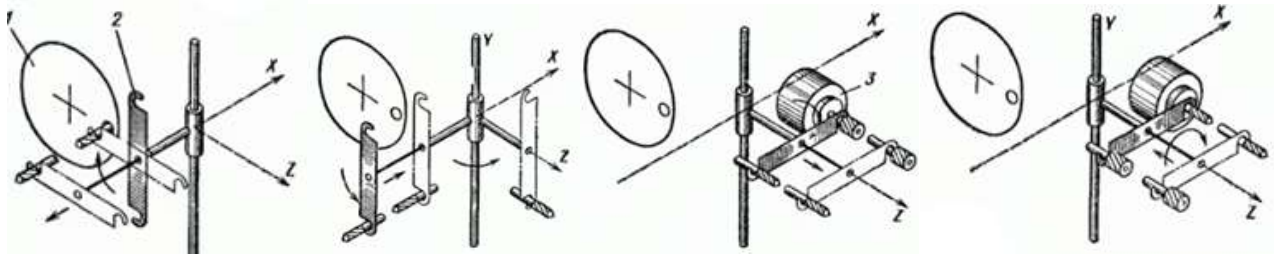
Порядок роботи автооператора: 1- магазин; 2- автооператор; 3- шпиндель
